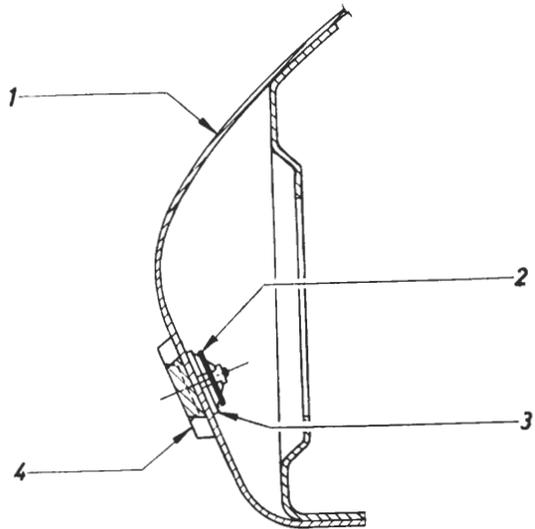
Buchstaben „Opel“ auf Motorhaube
